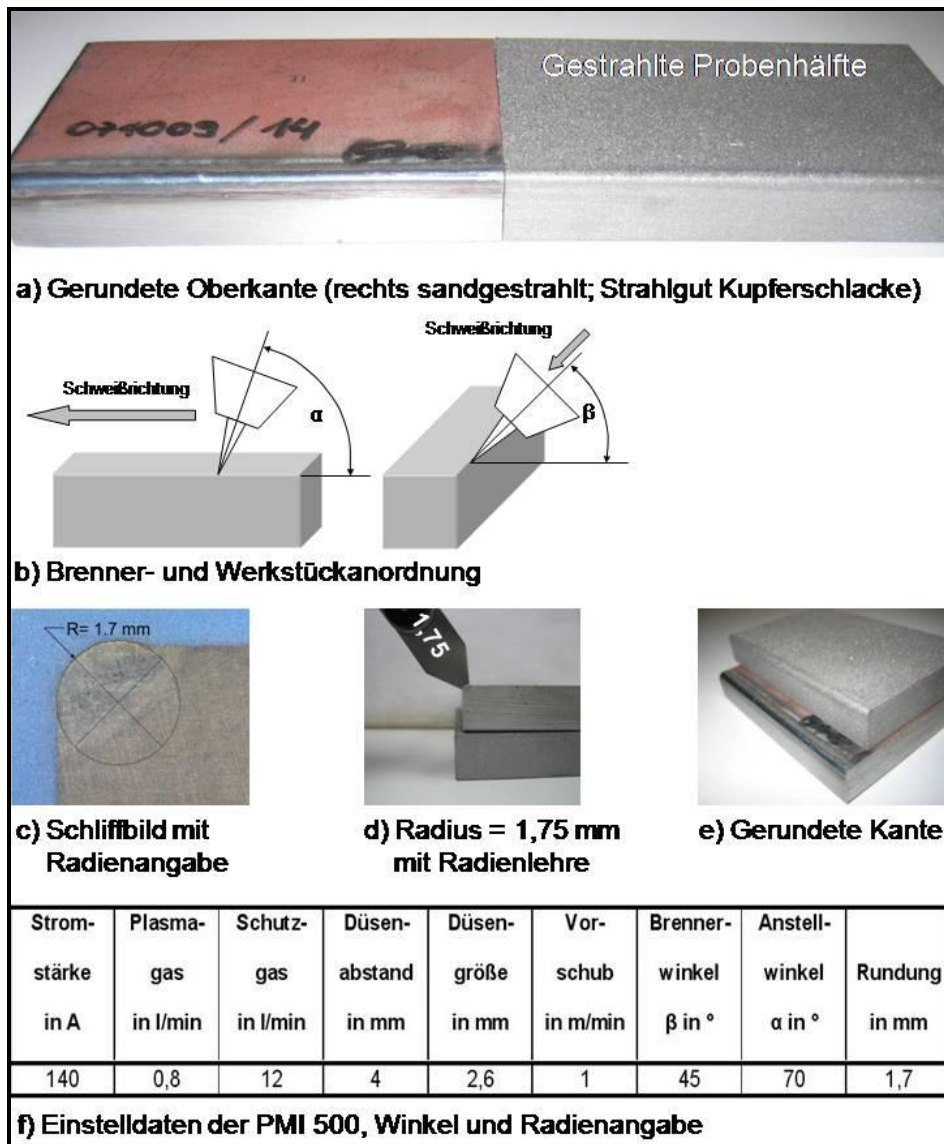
Mittels Plasmaschweißverfahren gerundete Oberkante
